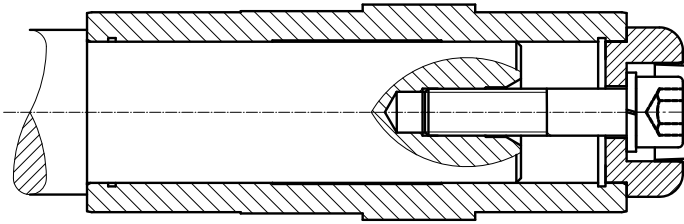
Getriebe auf Welle mit Anlageschulter mit Befestigungselement befestigt
